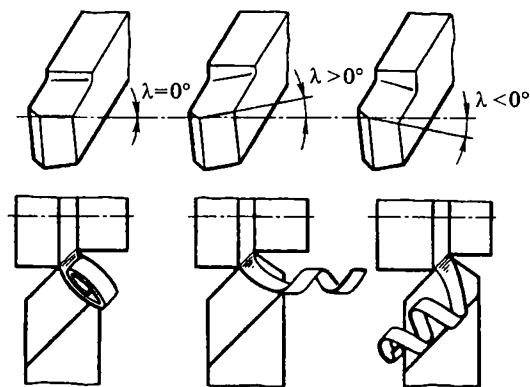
Углы наклона главной режущей кромки и направляющие схода стружки
